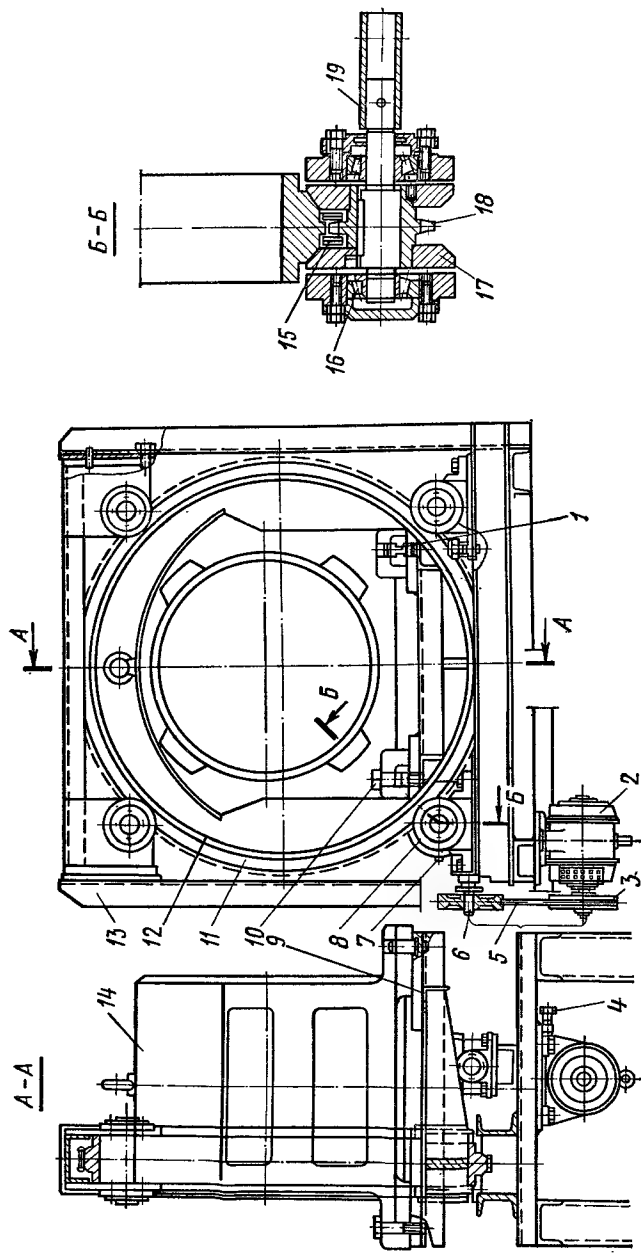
Кантователь для обмотки статоров 8 и 9-го габаритов
